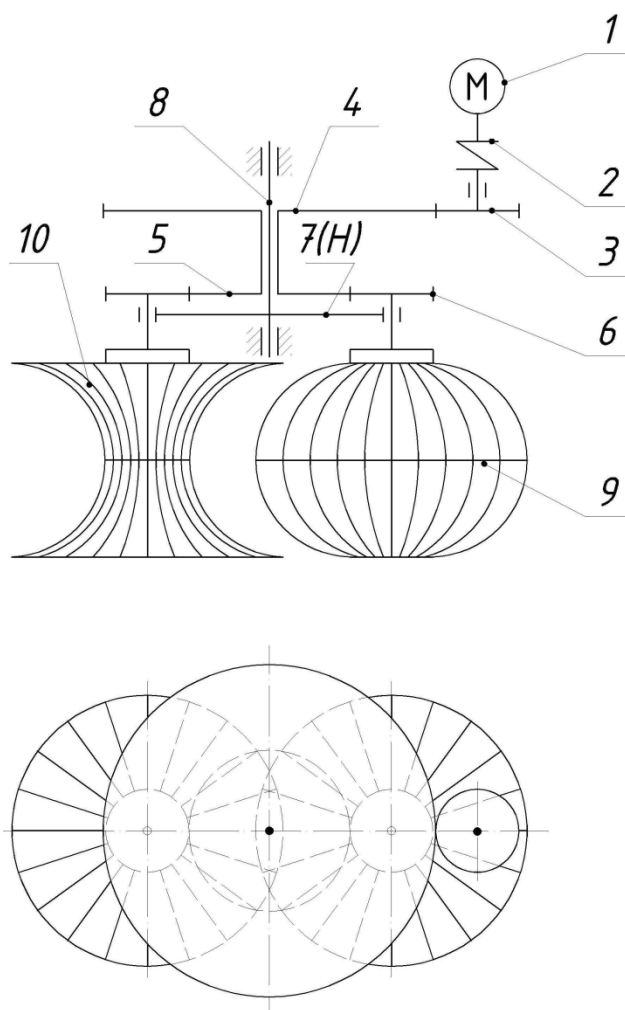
Кинематическая схема двухсателлитного планетарного механизма для привода рабочего органа миксера, где: 1 — электродвигатель, 2 — муфта, 3 — шестерня, 4 — простое зубчатое колесо, 5 — солнечное колесо, 6 — сателлит, 7 (H) — водило, 8 — вал, 9 — месильный орган венчика сжатого эллипсоидального вращения; 10 — месильный орган венчика однополюсного гиперболоида вращения
